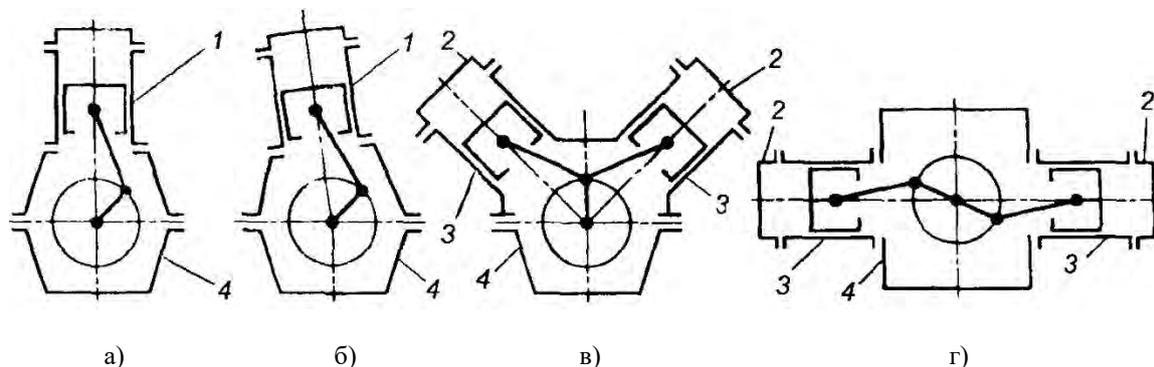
Варианты расположения цилиндров двигателя:
